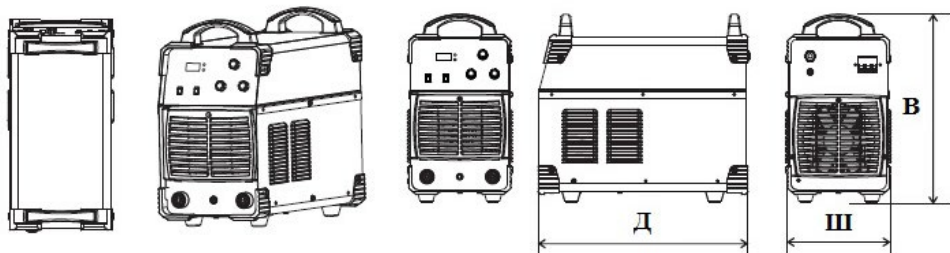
Внешний вид и размеры аппарата (мм)
